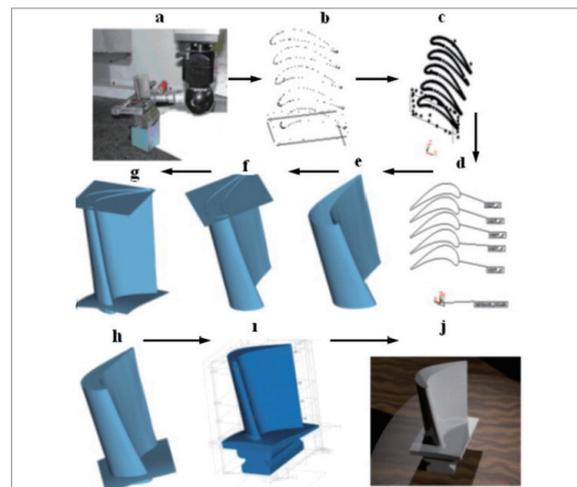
Reverse Engineering 3D CAD Model 생성 단계 예2 (제조분야)
